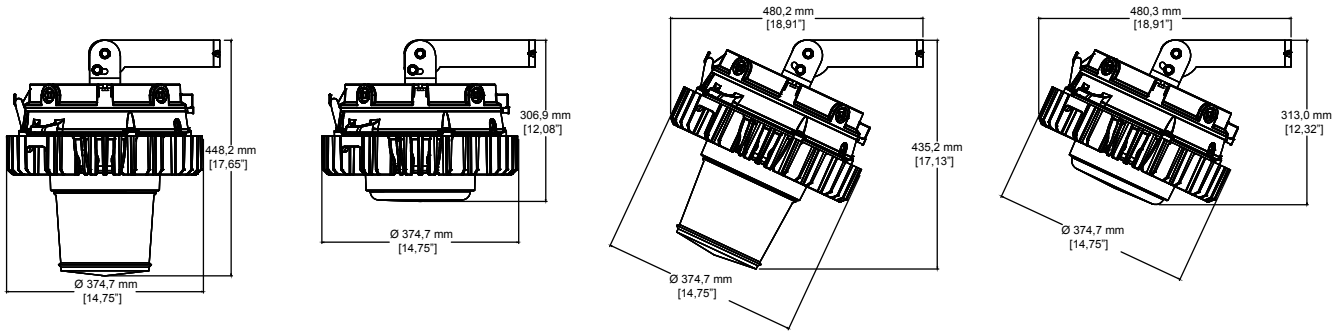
DÉTAILS DE LA HOTTE DE PLAFOND
